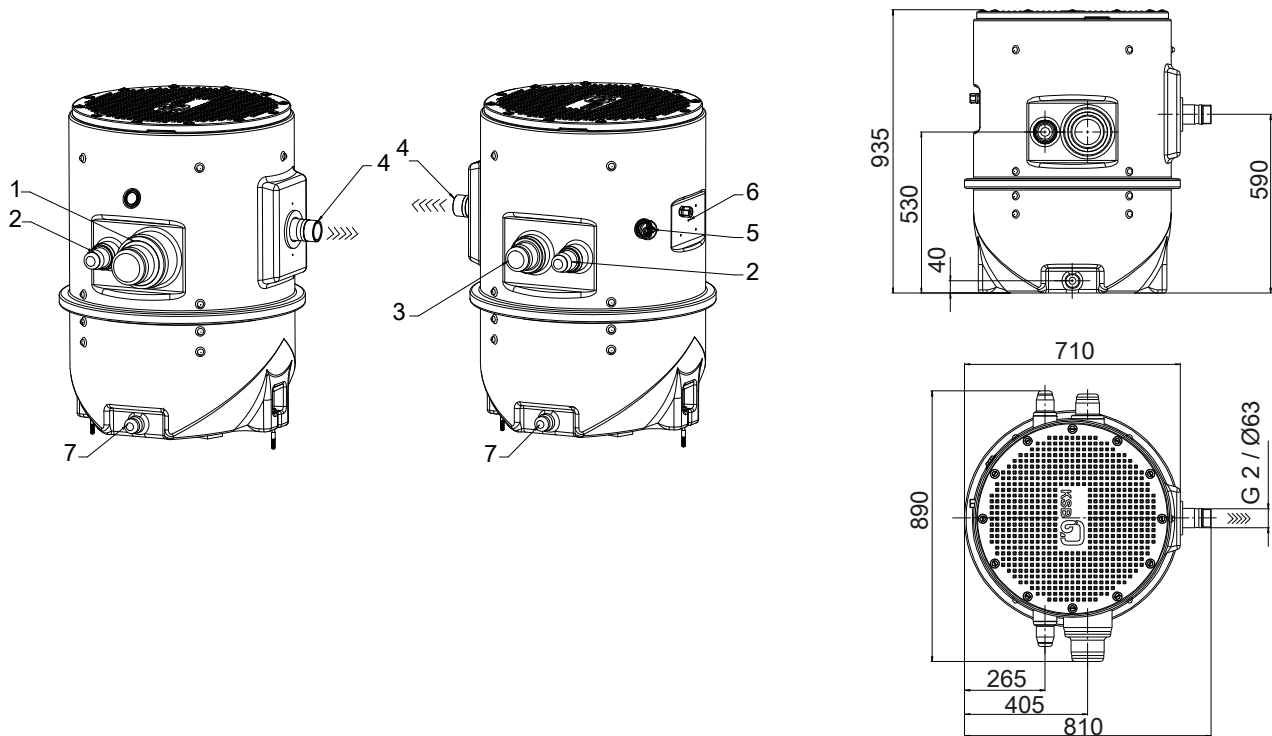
Conexiones y dimensiones de la instalación elevadora doble
